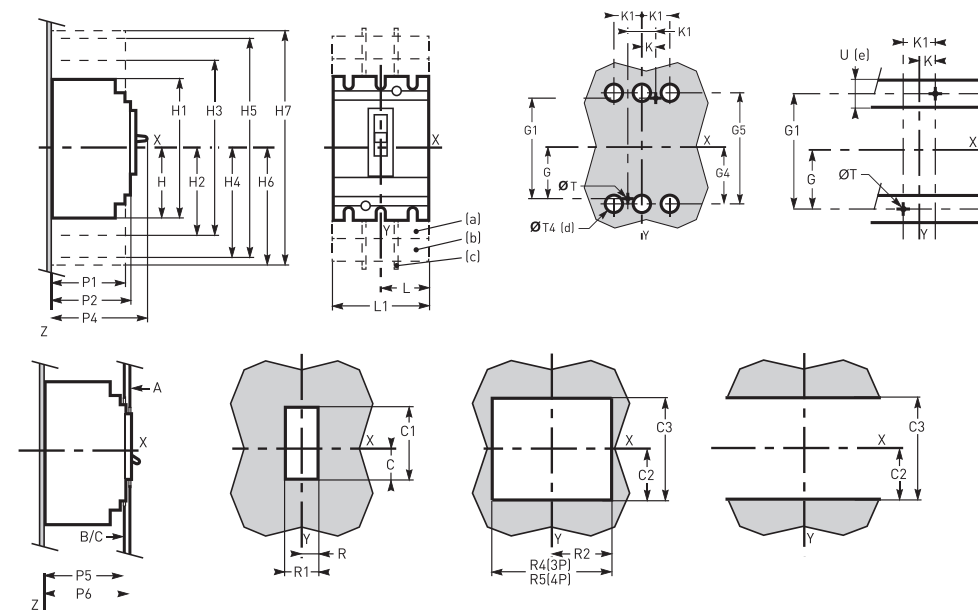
Габаритные и установочные размеры автоматических выключателей ВА-99С 100/160/250/400/630
